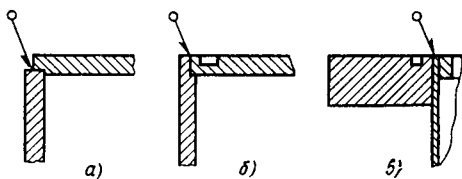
Конструкции угловых сварных соединений:
